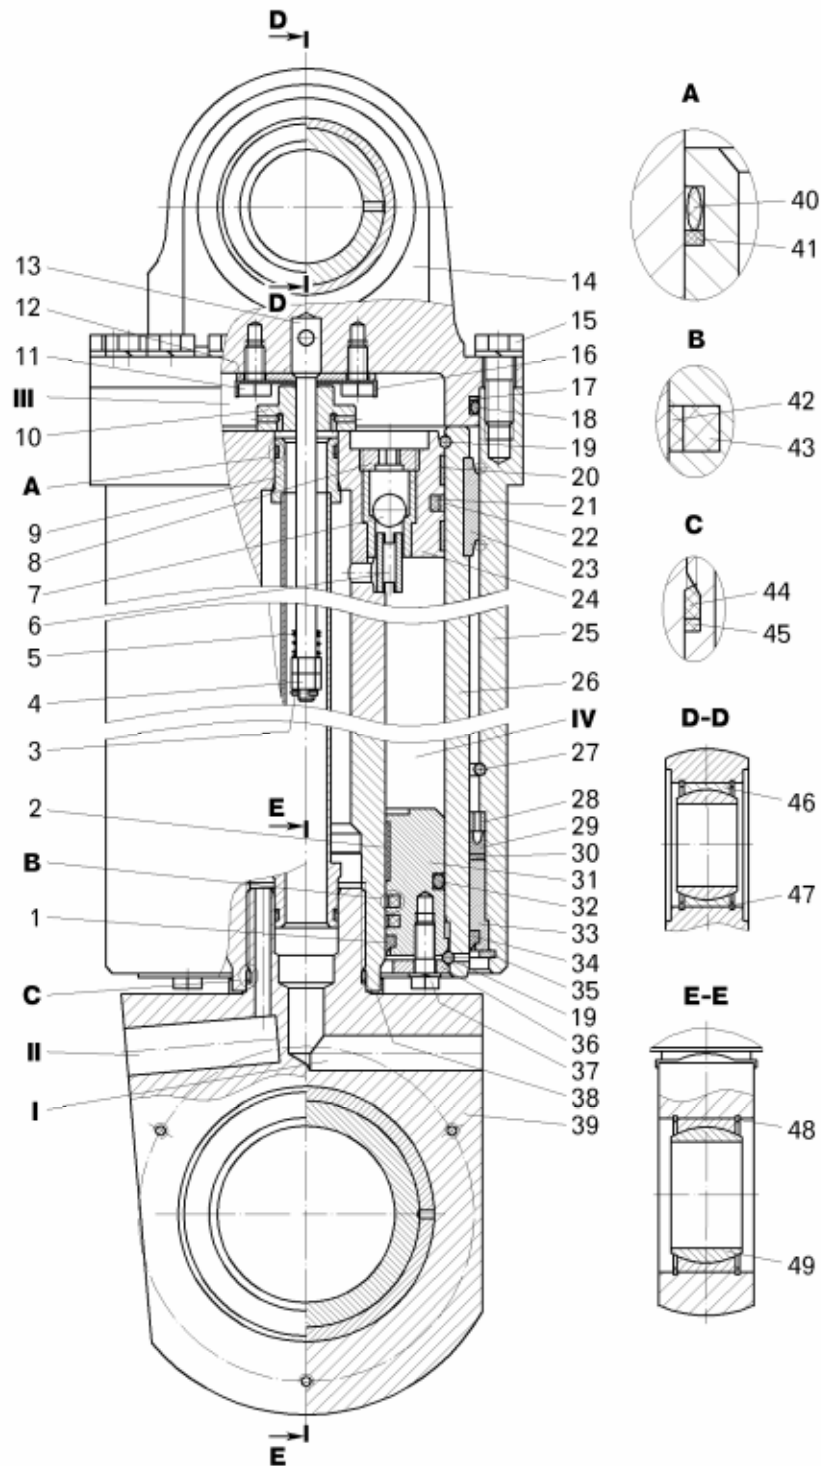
Цилиндр опрокидывающего механизма:
